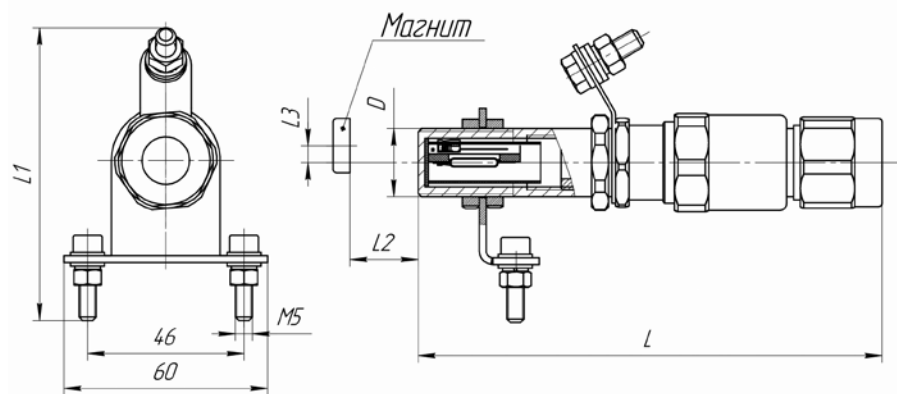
Взрывозащищенный магнитный выключатель (геркон) ВЭЛАН-SENSOR-ВГ
